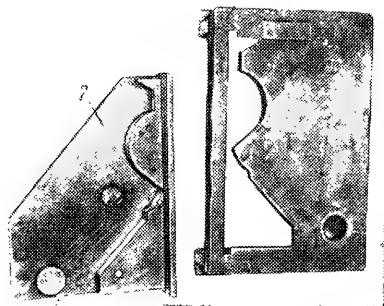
Штампы для изготовления дугогасительных перегородок:
